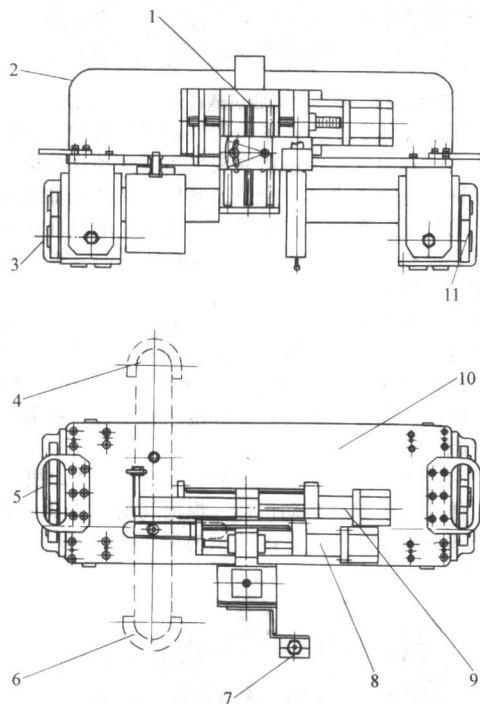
BIPT-3 焊接机器人主体(焊车)结构简图
